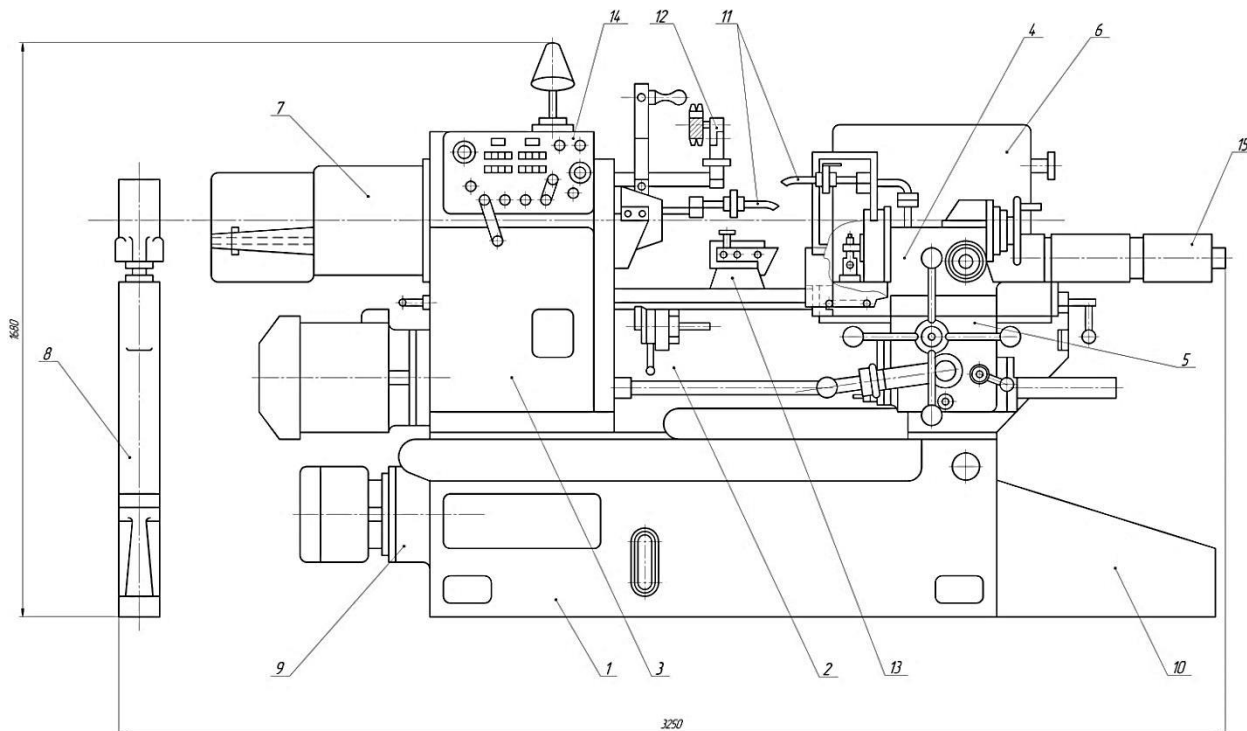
Загальний вид базової моделі верстата 1341
